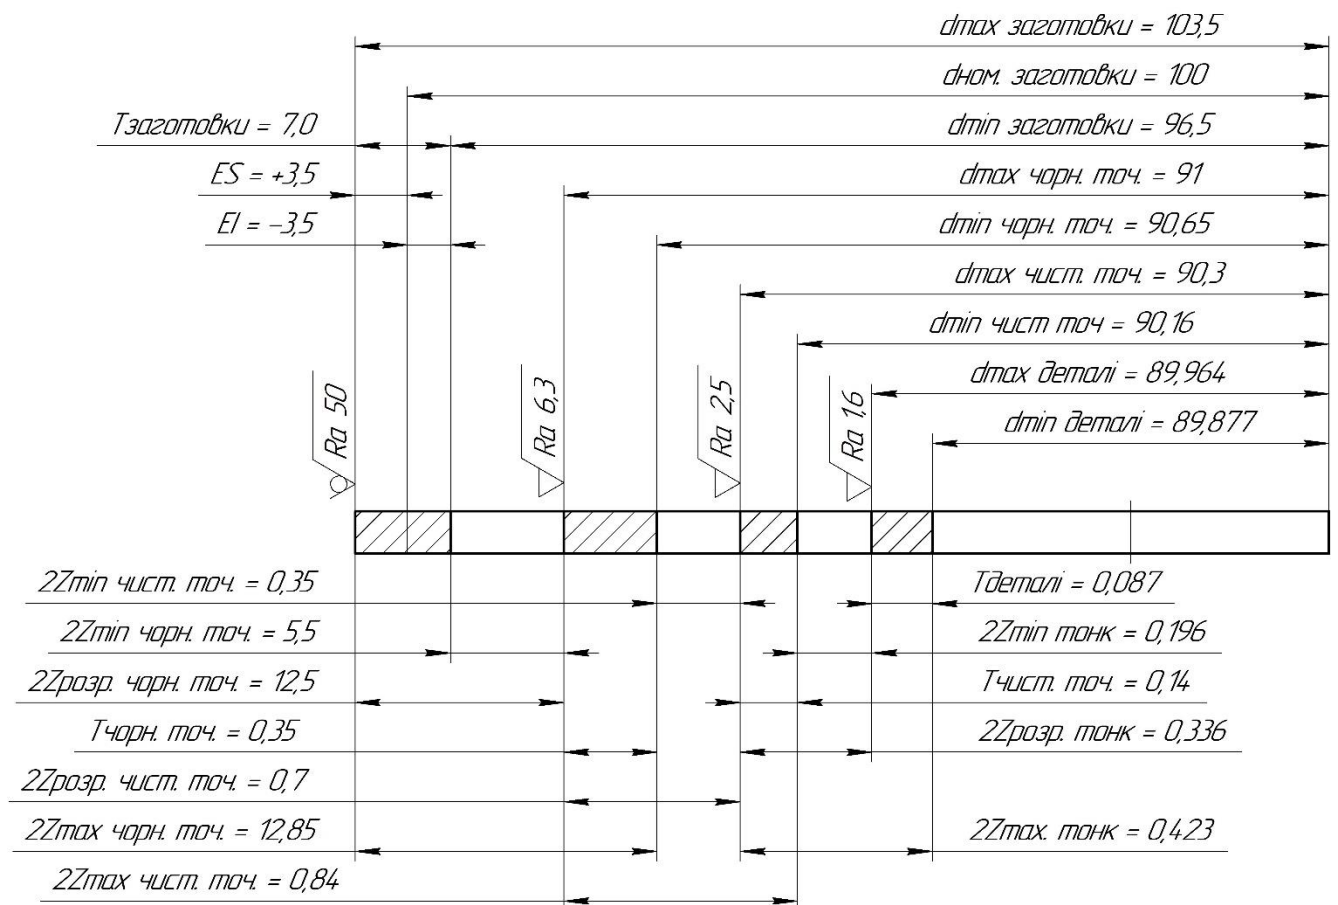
Схема розташування припусків і допусків на обробку поверхні діаметром 90f9(-0,036; -0,123) мм
